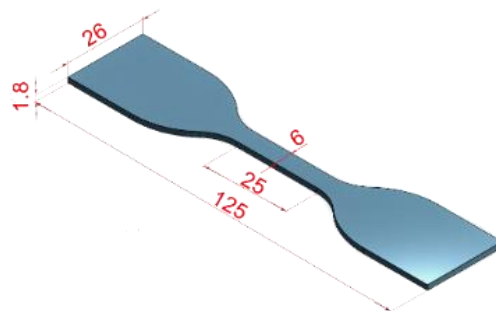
Dimensions de l'éprouvette (mm) selon la norme ASTM D638.
